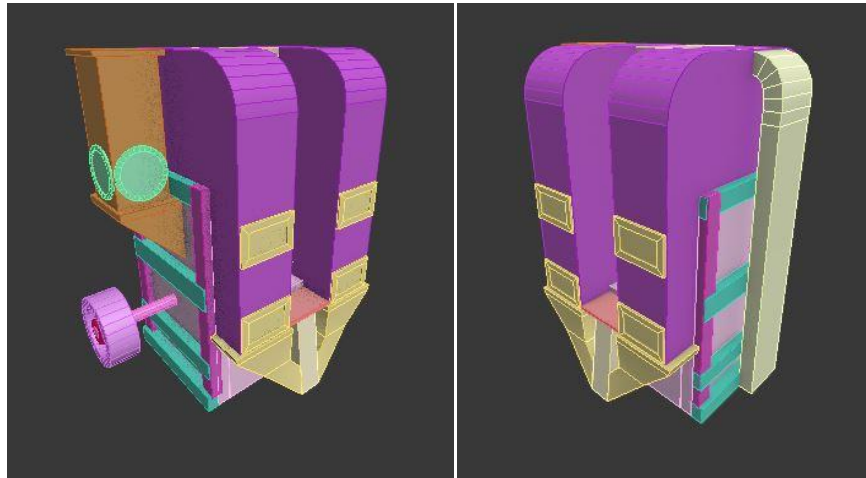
Vistas frontales del modelado de la despuntadora.
